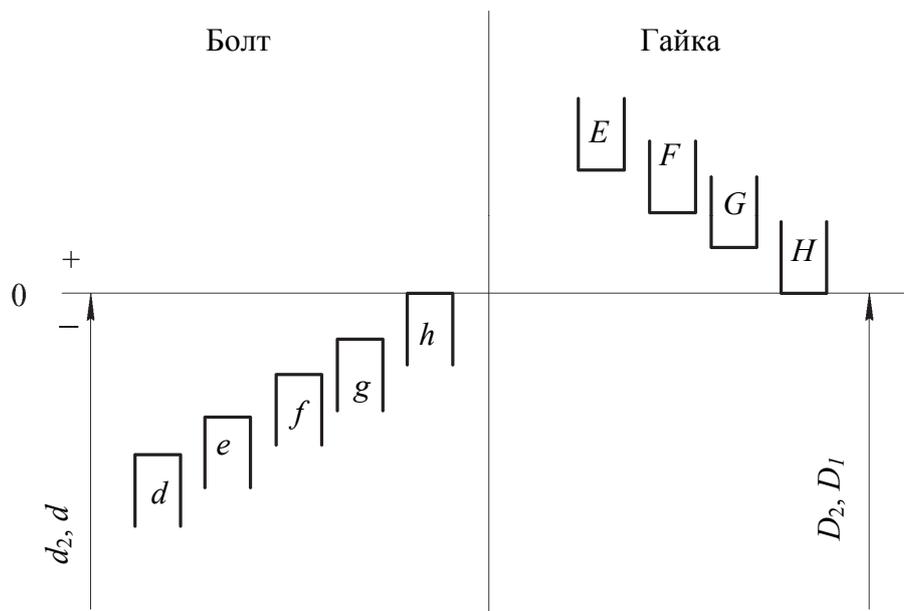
Схема расположения основных отклонений резьбы для посадок с зазором
